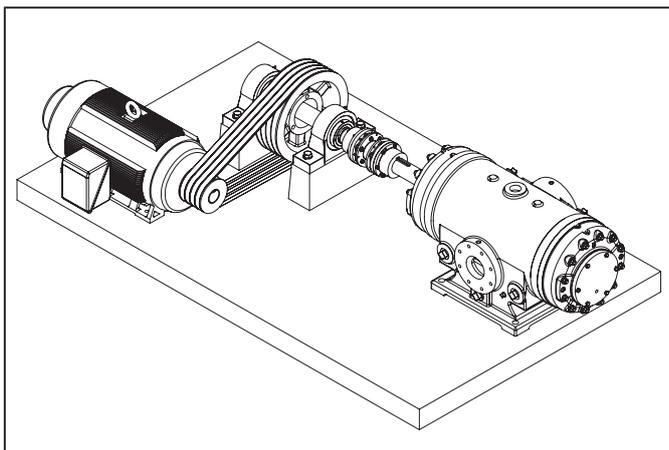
Типовое расположение ременных передач с цокольными подшипниками и промежуточным валом.
